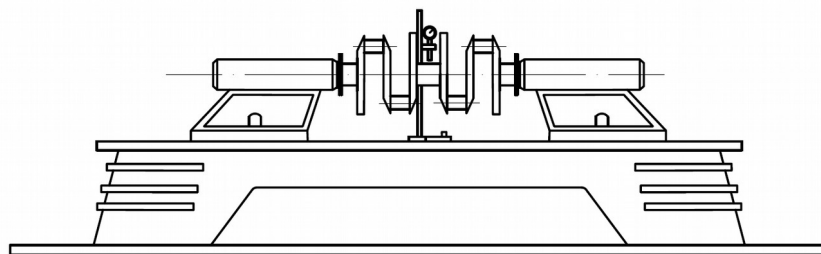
Прилад для перевірки колінчатого вала на биття в центрах
